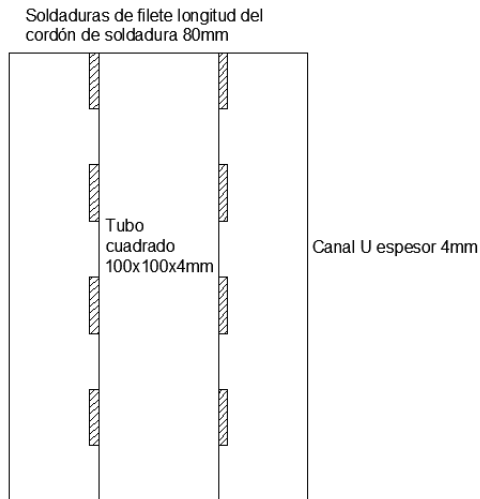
(Esquema soldadura del carro transportador)
